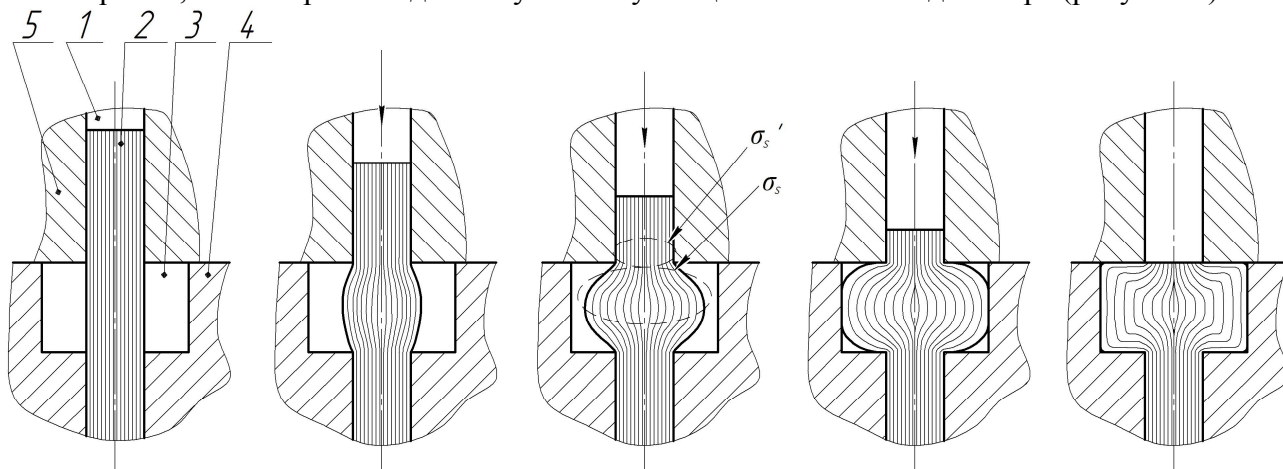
Строение волокон поковки в процессе деформации металла: 1 – пуансон; 2 – заготовка; 3 – полость штампа; 4 – матрица; 5 – подпружиненная втулка
